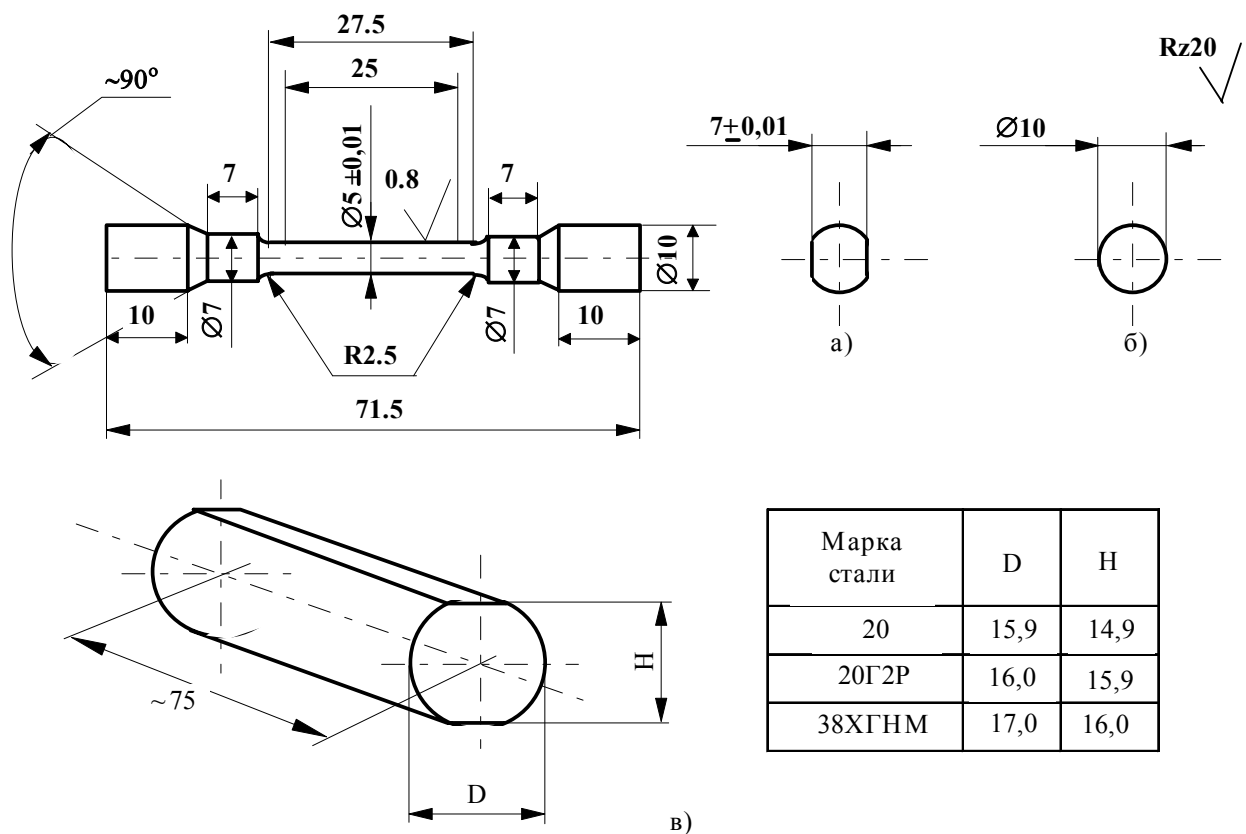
Форма и размеры образцов для испытаний по схемам 1 и 2.
